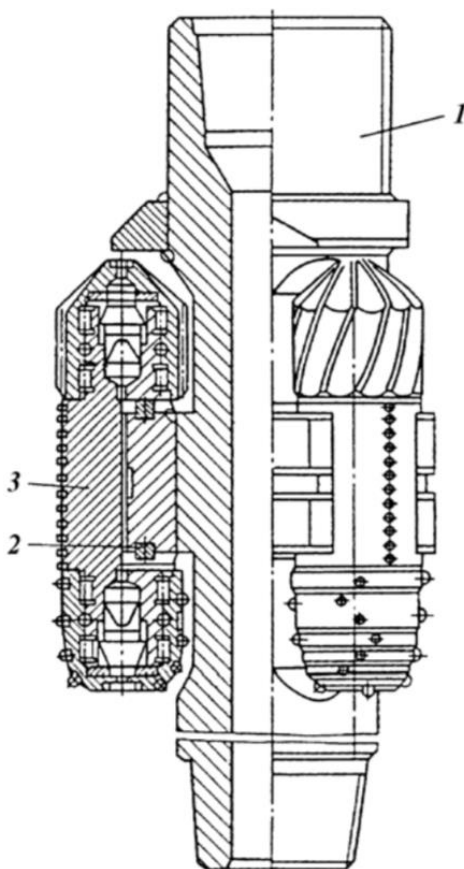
Схема шарошечного калибратора типа КШУ: 1 – корпус; 2 – клинья; 3 – узел калибрующий
